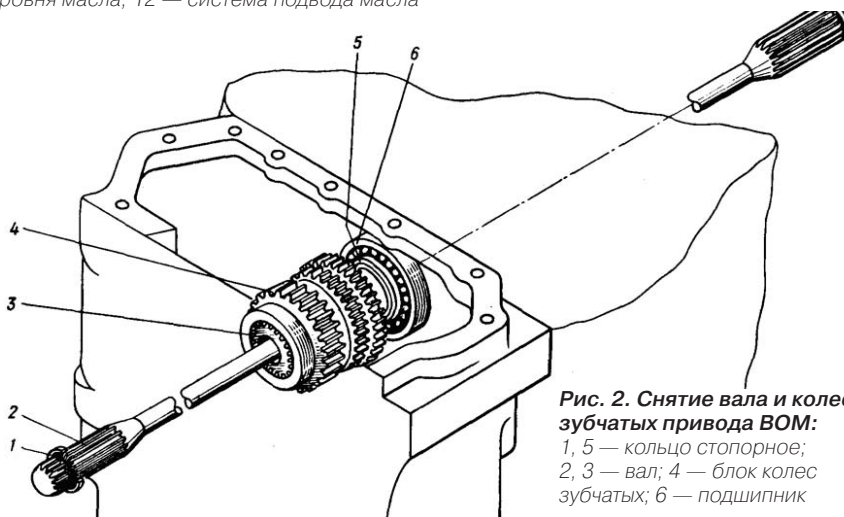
Снятие вала и колес зубчатых привода ВОМ: 1, 5 — кольцо стопорное; 2, 3 — вал; 4 — блок колес зубчатых; 6 — подшипник
